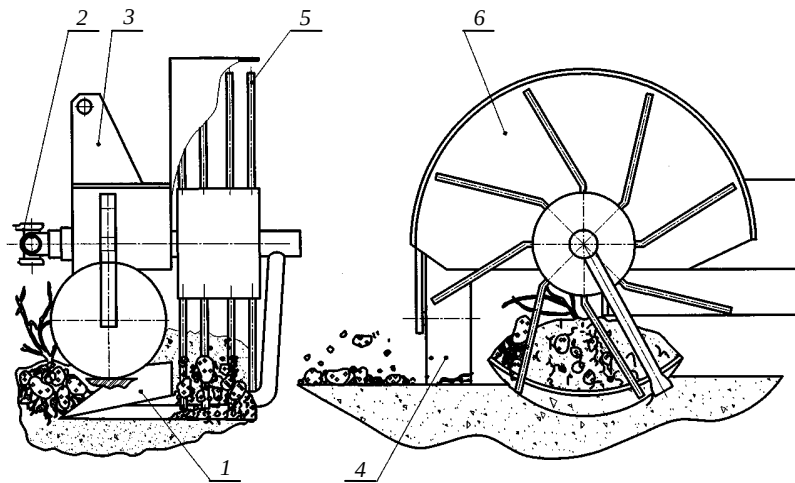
Конструктивно-технологічна схема картоплекопача КТН-1,0М: 1 – леміш; 2 – механізм приводу; 3 – навіска; 4 – колесо опорне; 5 – ротор; 6 – щиток.
